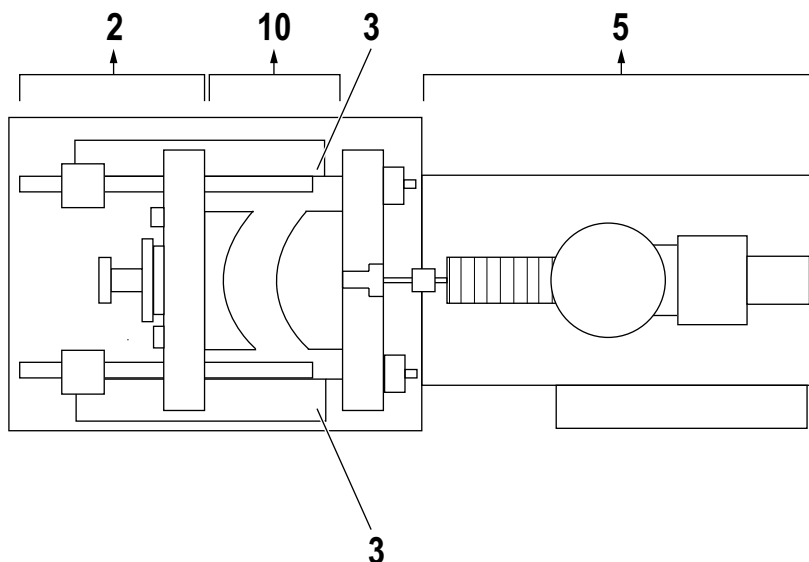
Zonas de peligro de una máquina de moldeo por inyección (vista superior)
